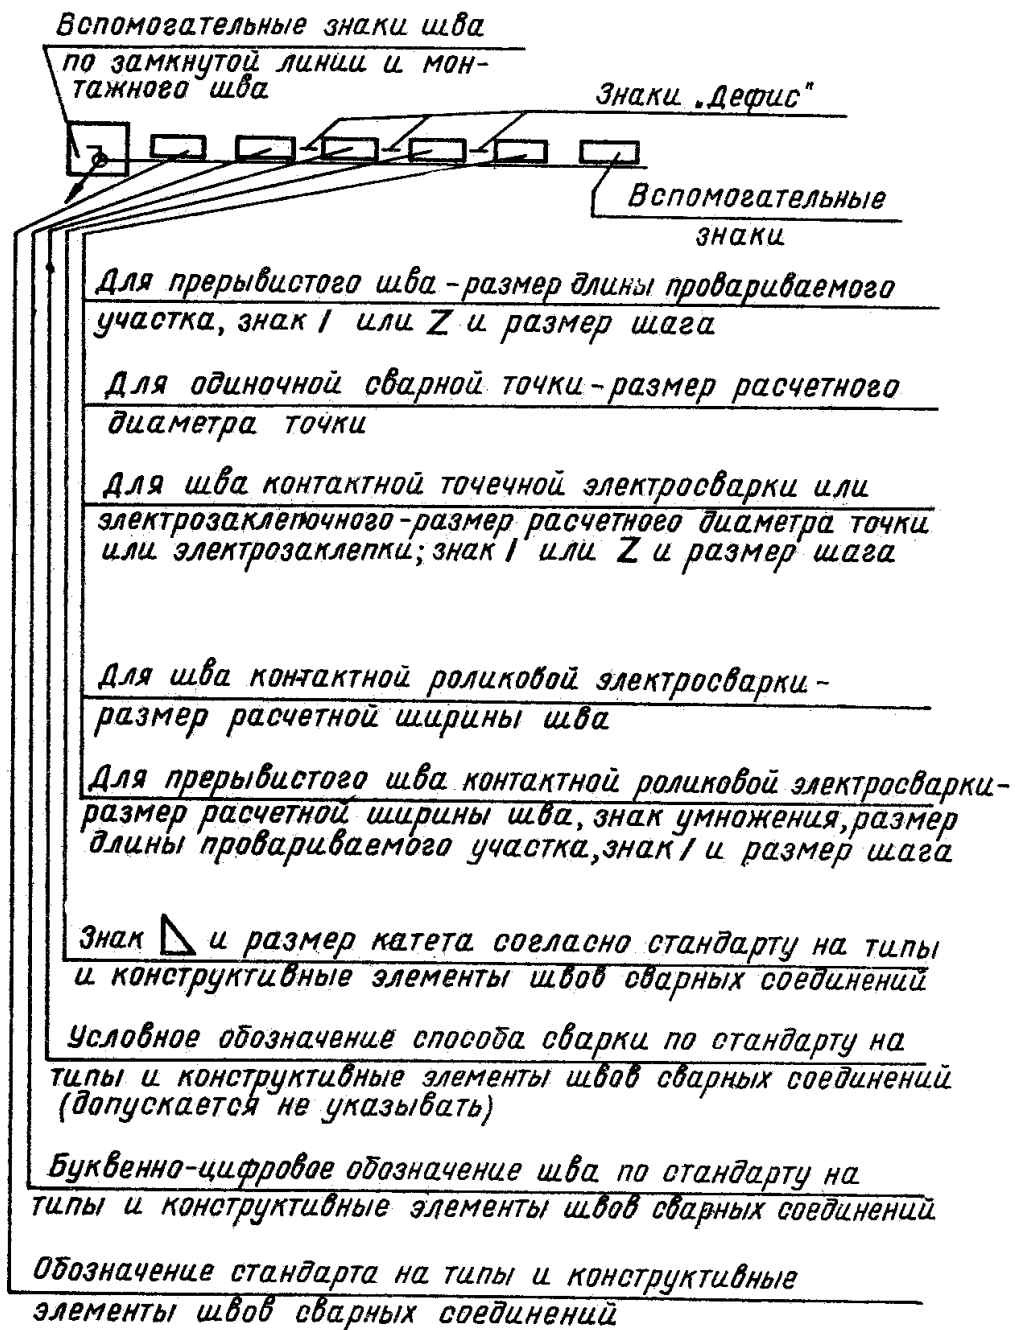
Структурная схема условного обозначения стандартного шва (одиночной сварной точки)
